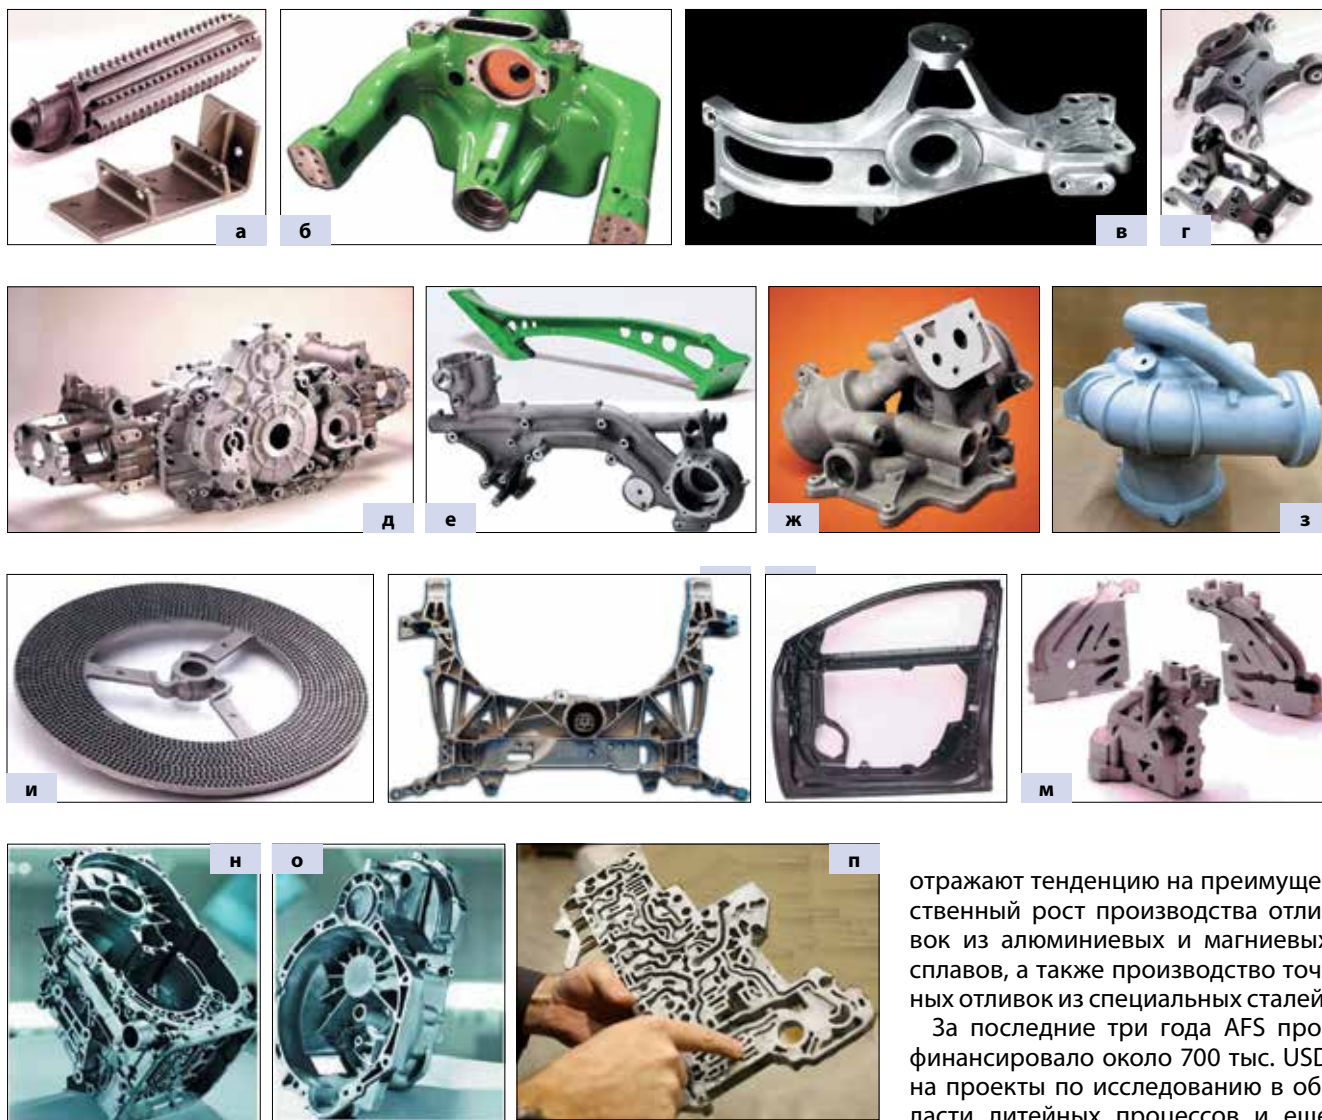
Отливки из фотогалерей зарубежных сайтов литейной тематики: а – цепной ролик и кронштейн; б – корпус привода трактора; в – стальная подвеска двигателя; г – нижний рычаг и кронштейн кабины тяжелого грузовика; д – картер в сборе; е – штанга и термальный регулятор; ж, з – насосы из алюминиевых сплавов; и – диск из серого чугуна; к – деталь переднего подрамника; л – задняя дверь из магния; м – алюминиевый коллектор; н, о, п – сложные отливки, полученные литьем под давлением алюминиевых сплавов.
